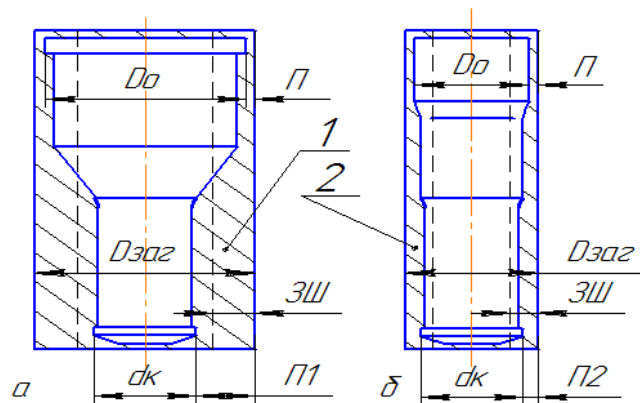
Залежність розмірів вихідної заготовки від особливостей конструкції пуансона.  $3Ш$  – ширина здорової шкірки заготовки.
